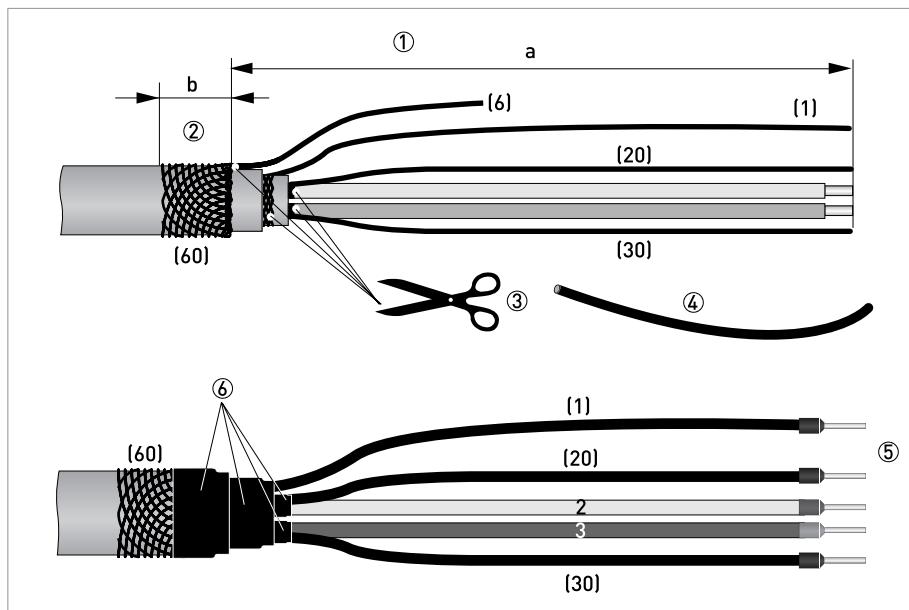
Сигнальный кабель В, подготовка для корпуса полевого исполнения
